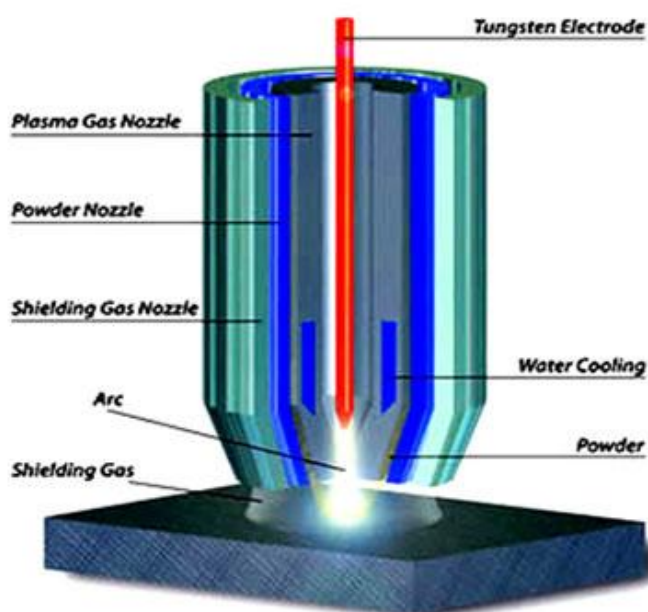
Ilustração esquemática do processo de soldagem PTAW, Plasma transferred arc welding utilizando adição de pó metálico (mining-technology.com).
